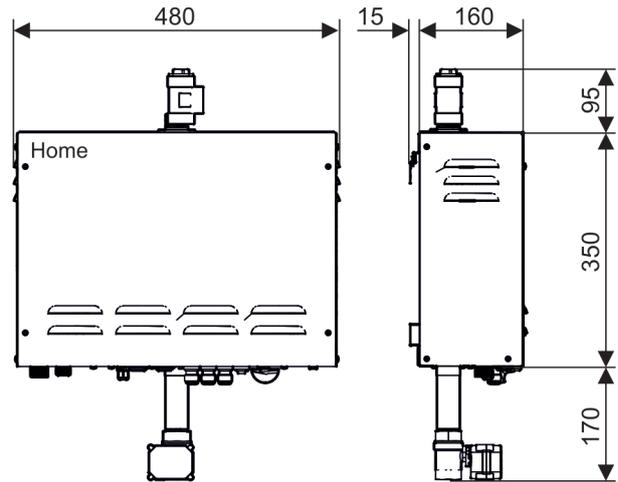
Dampferzeuger Typ Tylö Home Steam, Maßangaben in Millimetern
